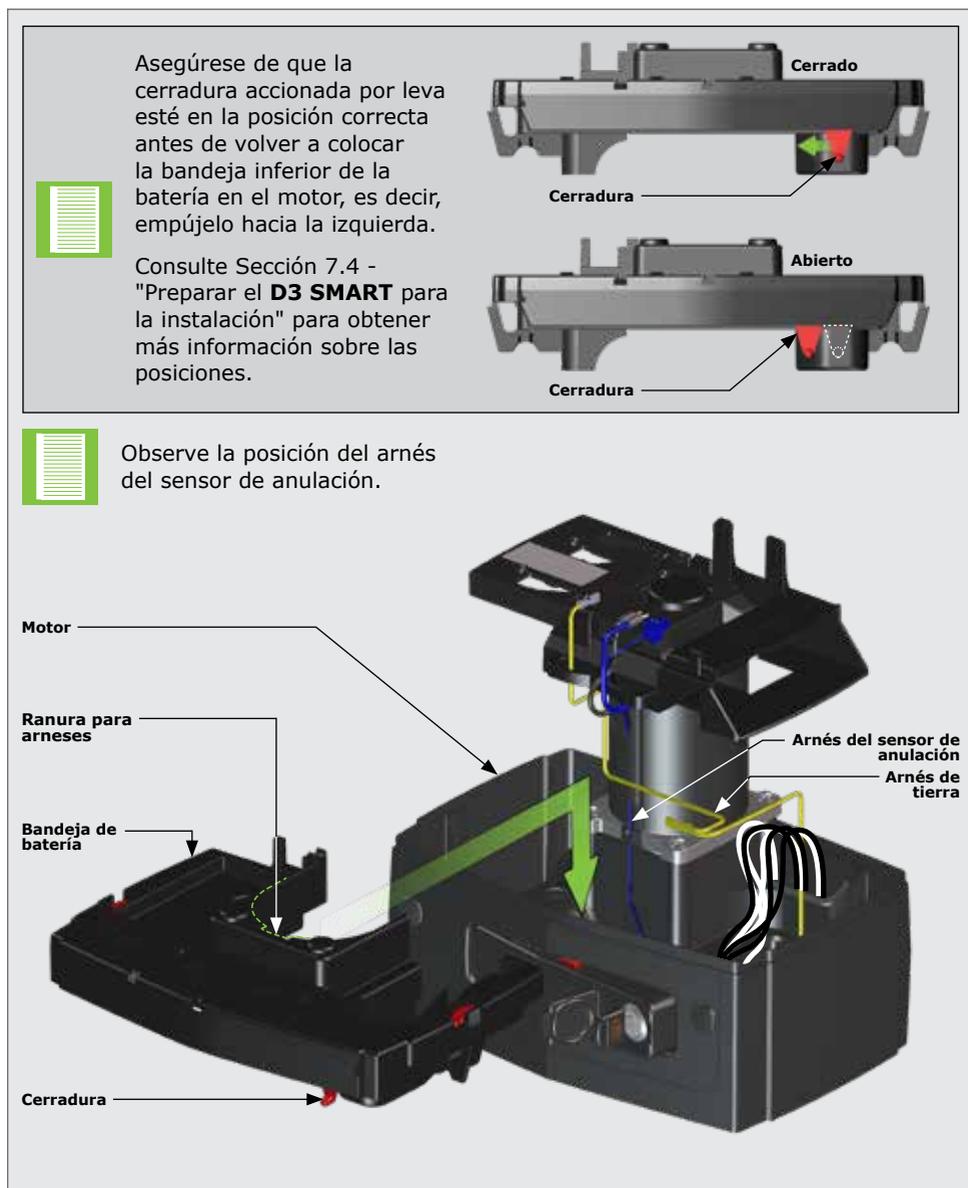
PONER LA BANDEJA INFERIOR DE LA BATERÍA
